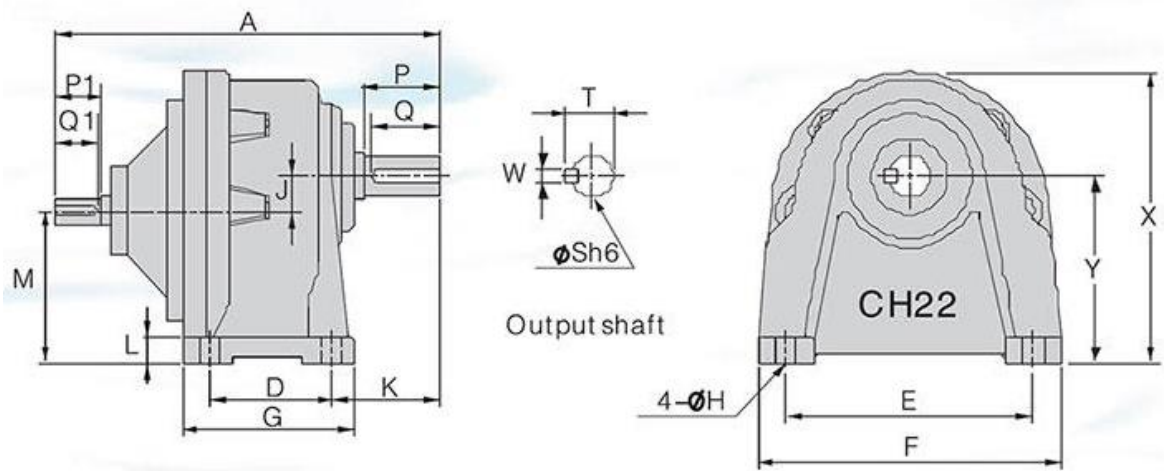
Figura isométrica y planos del reductor seleccionado. Tomado de Hangsin Motor, <http://garmotorreducer.com/2-1-horizontal-parallel-shaft-speed-reducer.html>, consultado 18 de noviembre (2020).
